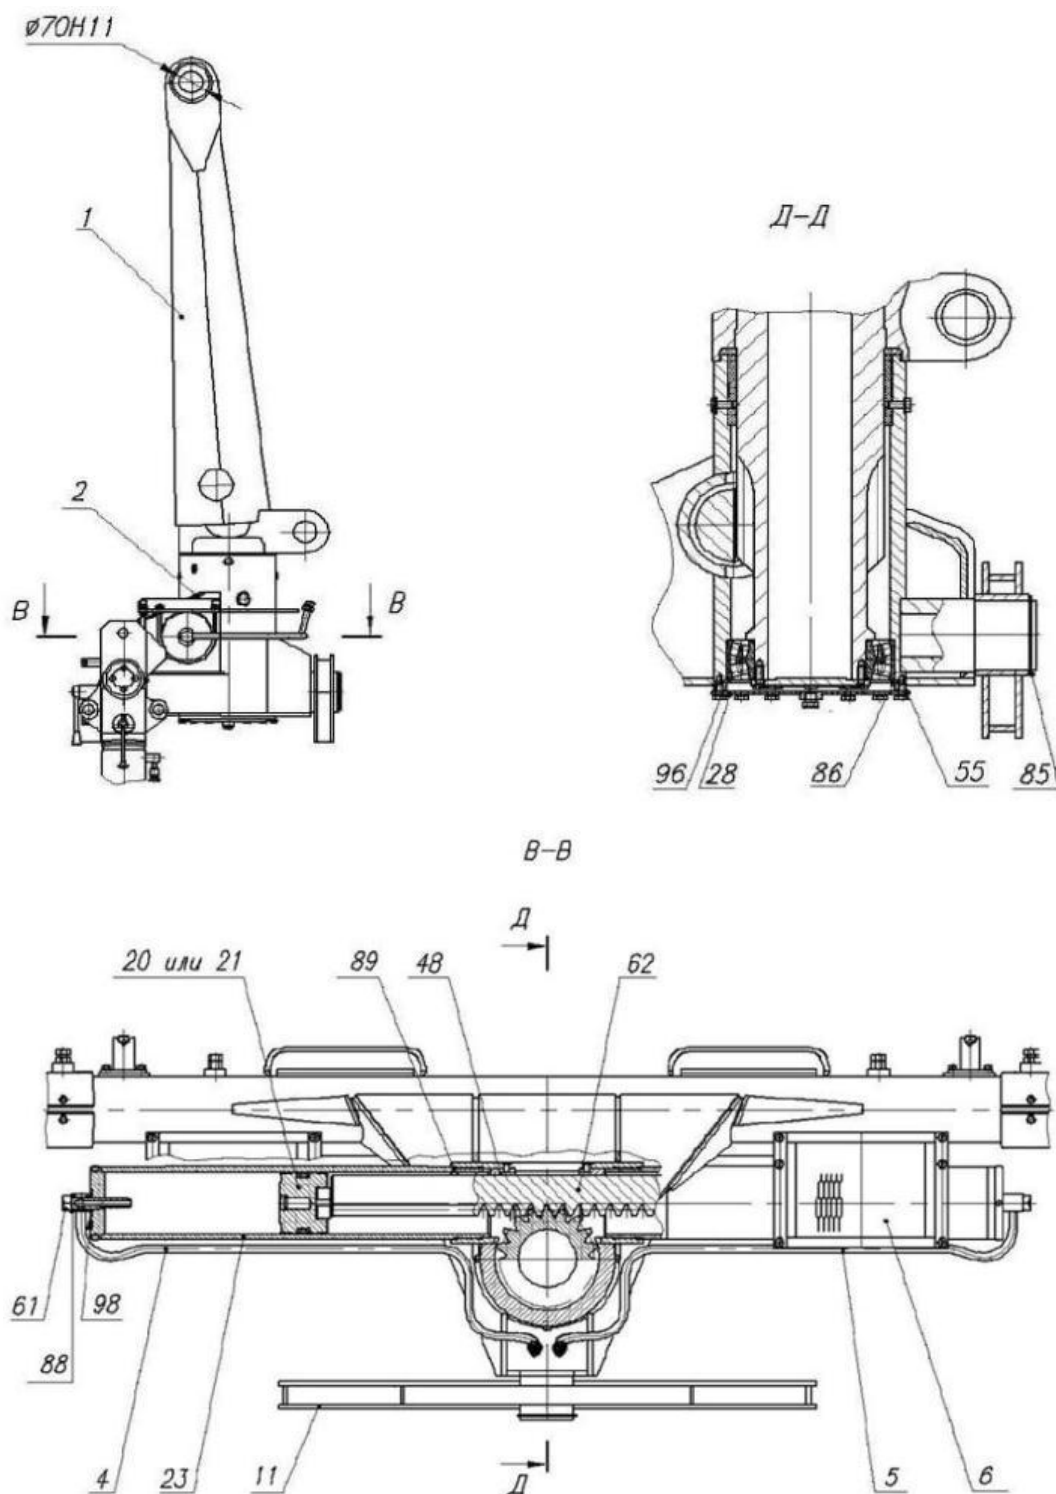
Сборочный чертёж опорно-поворотного узла гидроманипулятора
